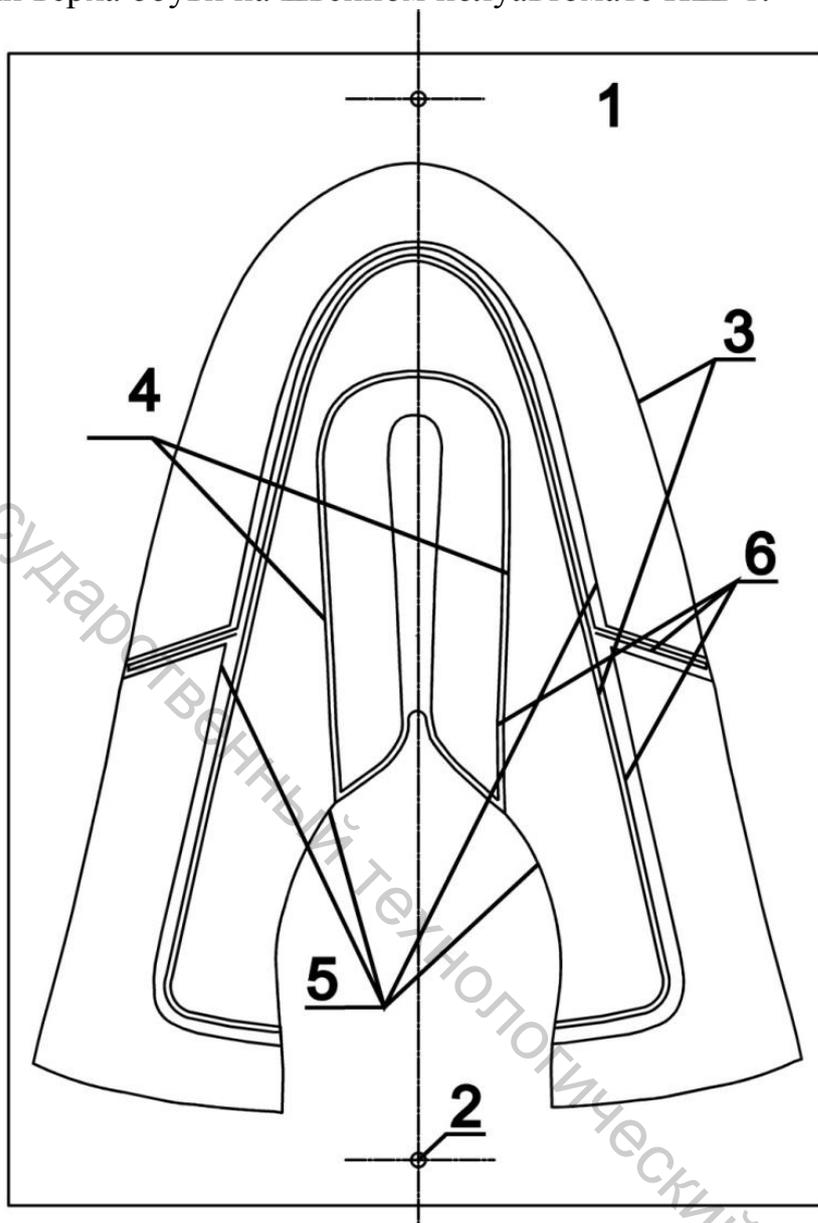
Кассета для сборки заготовки верха обуви:
